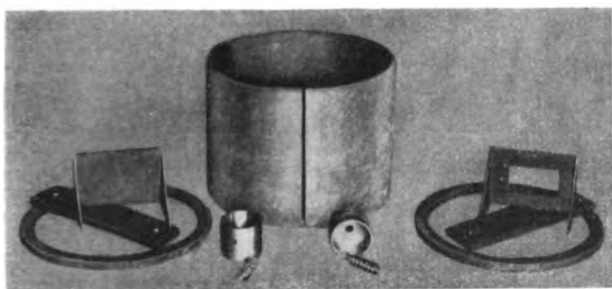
Teile des zu schweißenden Magnetgehäuses.
